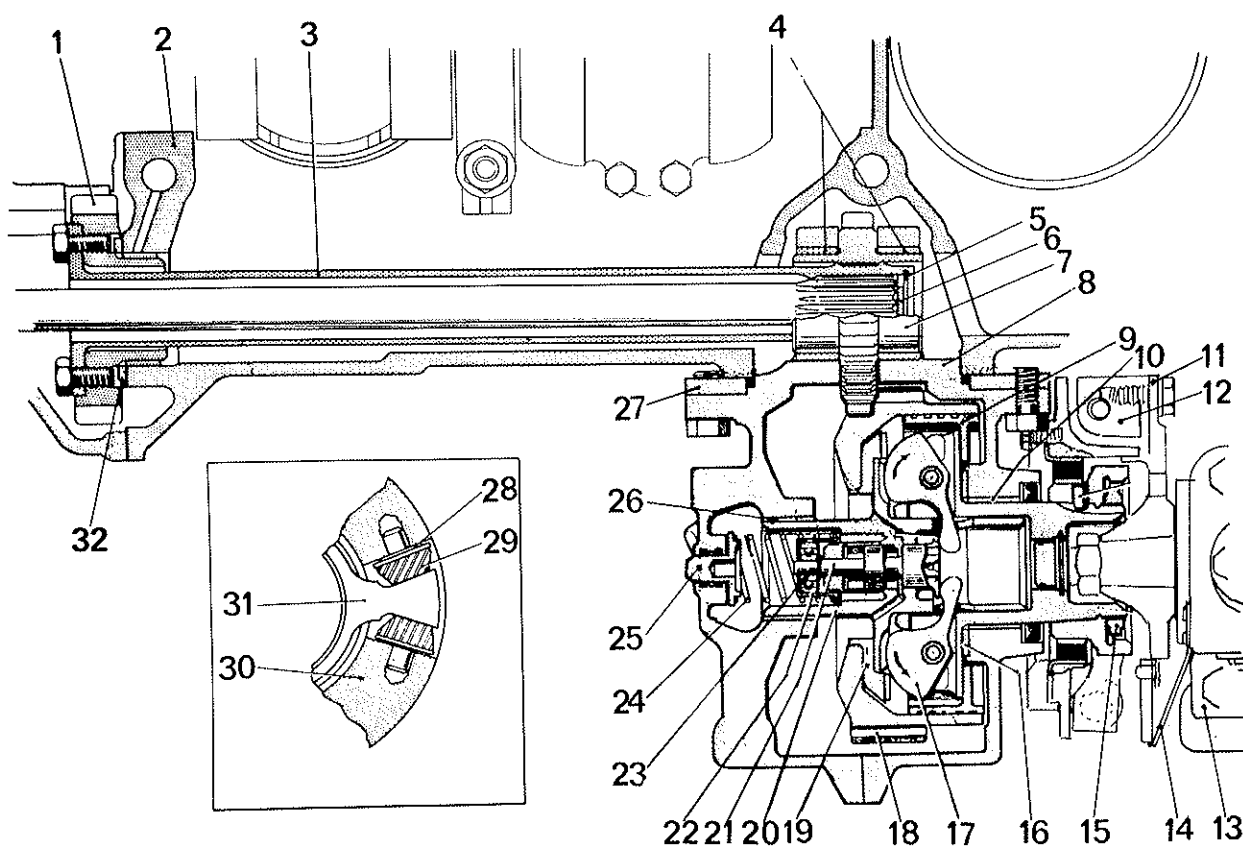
Insprutningspumpens drivanordning sedd ovanifrån
